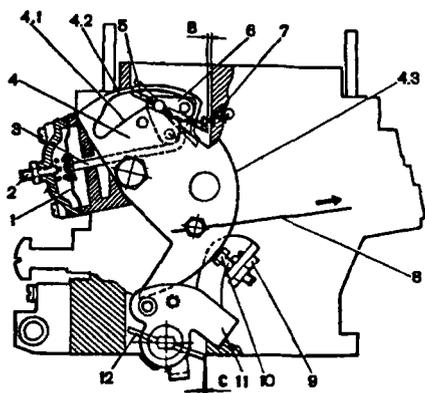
Пусковое устройство карбюратора 21053-1107010: 1 - диафрагма; 2 - регулировочный винт; 3 - шток диафрагмы; 4 - рычаг управления воздушной заслонкой; 4.1 - нижний профиль паза рычага 4 для ограничения максимального приоткрывания воздушной заслонки; 4.2 - верхний профиль паза, обеспечивающий механическое открытие воздушной заслонки; 4.3 - кромка рычага 4 для обеспечения пускового зазора дроссельной заслонки первой камеры; 5 - воздушная заслонка; 6 - рычаг воздушной заслонки; 7 - возвратная пружина воздушной заслонки; 8 - тяга привода воздушной заслонки; 9 - стопор регулировочного винта; 10 - регулировочный винт приоткрывания дроссельной заслонки первой камеры; 11 - рычаг привода дроссельных заслонок; 12 - дроссельная заслонка первой камеры
